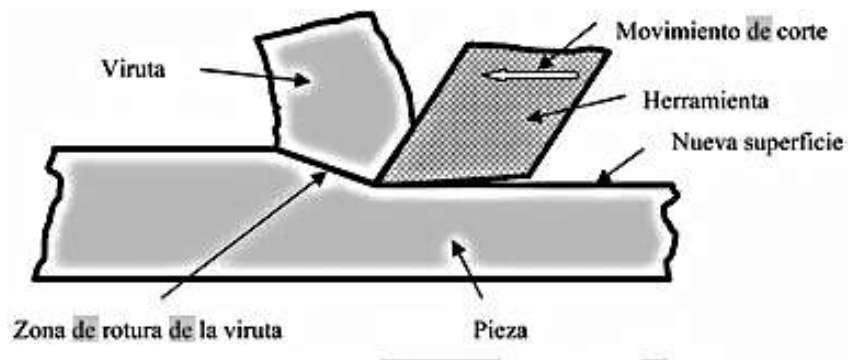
Esquema de mecanizado por arranque de viruta [12]
